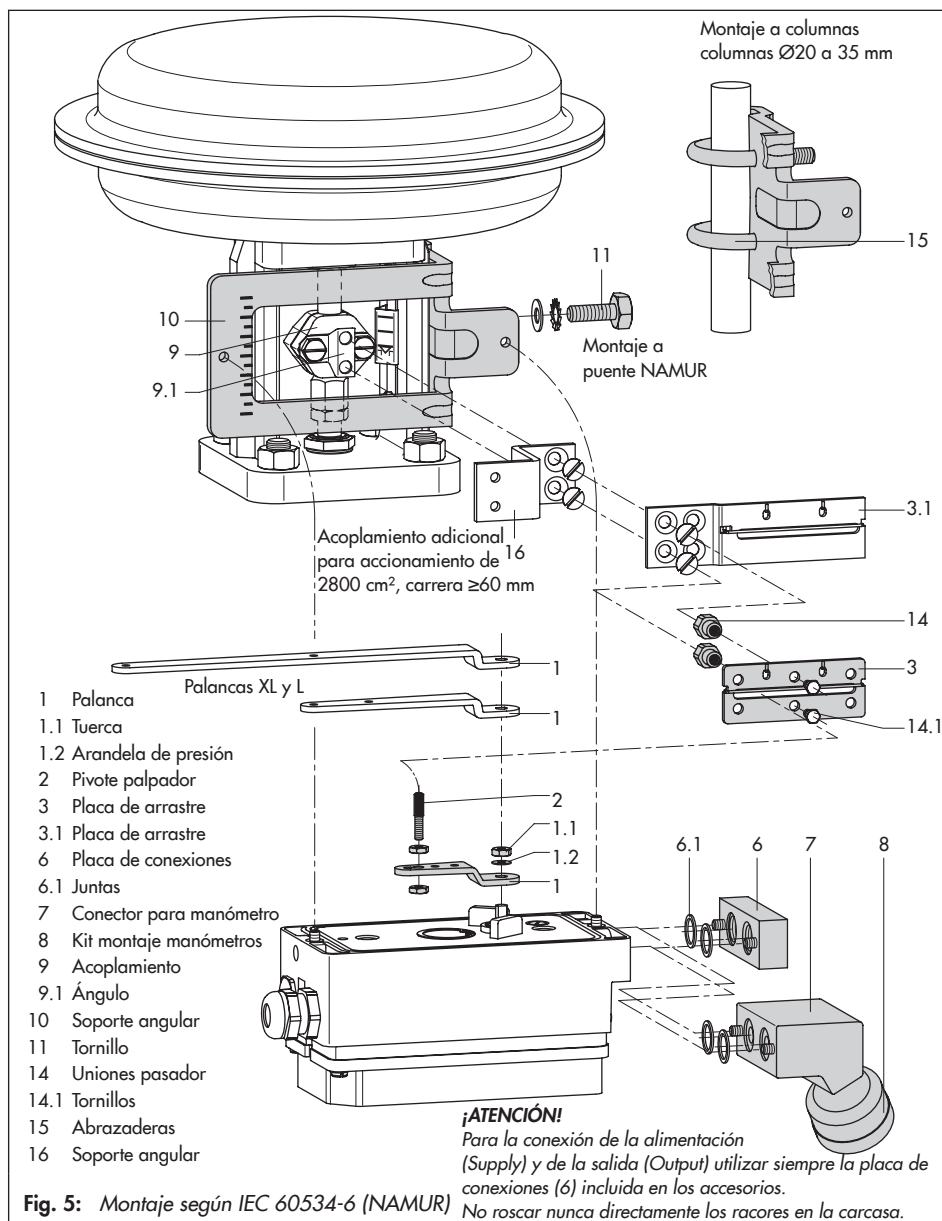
Montaje según IEC 60534-6 (NAMUR)
